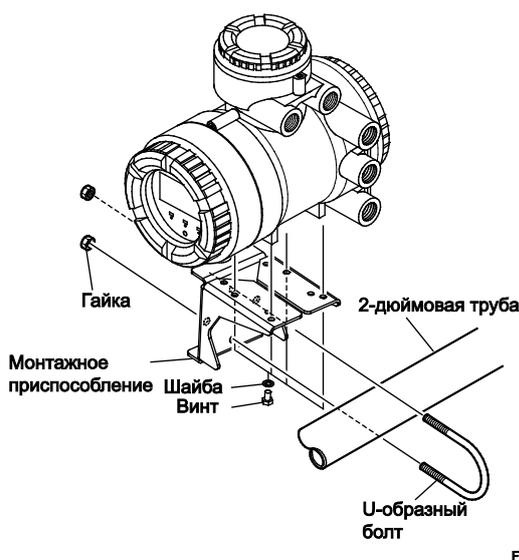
Монтаж на горизонтальной 2-дюймовой трубе
